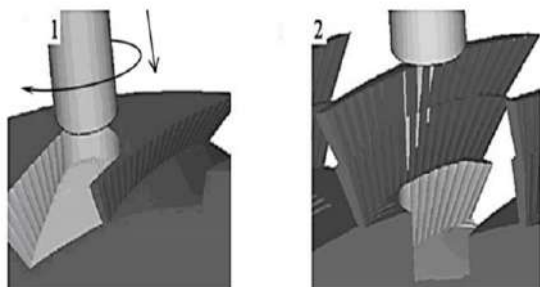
Плунжерное фрезерование межлопаточного канала [18]:
